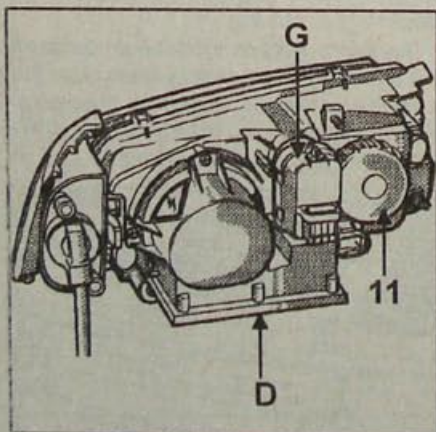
Расположение электронного блока (D), исполнительного механизма (G) для регулировки света фар по высоте и крышки (11)
